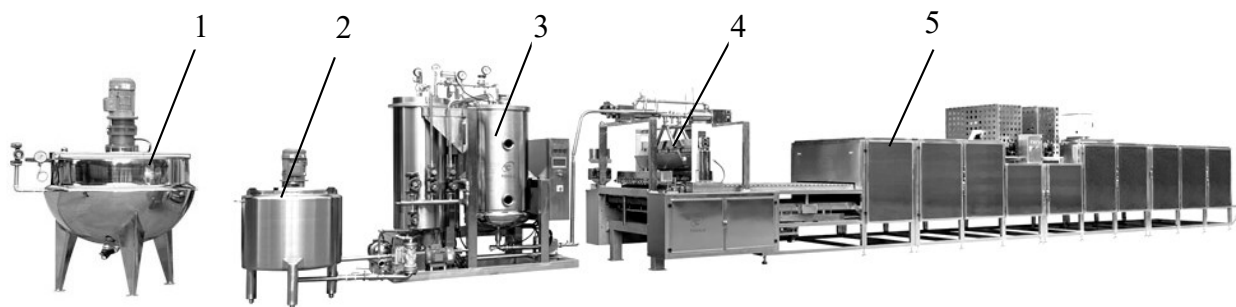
Лінія виробництва желейних цукерок Ningbo Youlu Machinery Technology Co [3].
